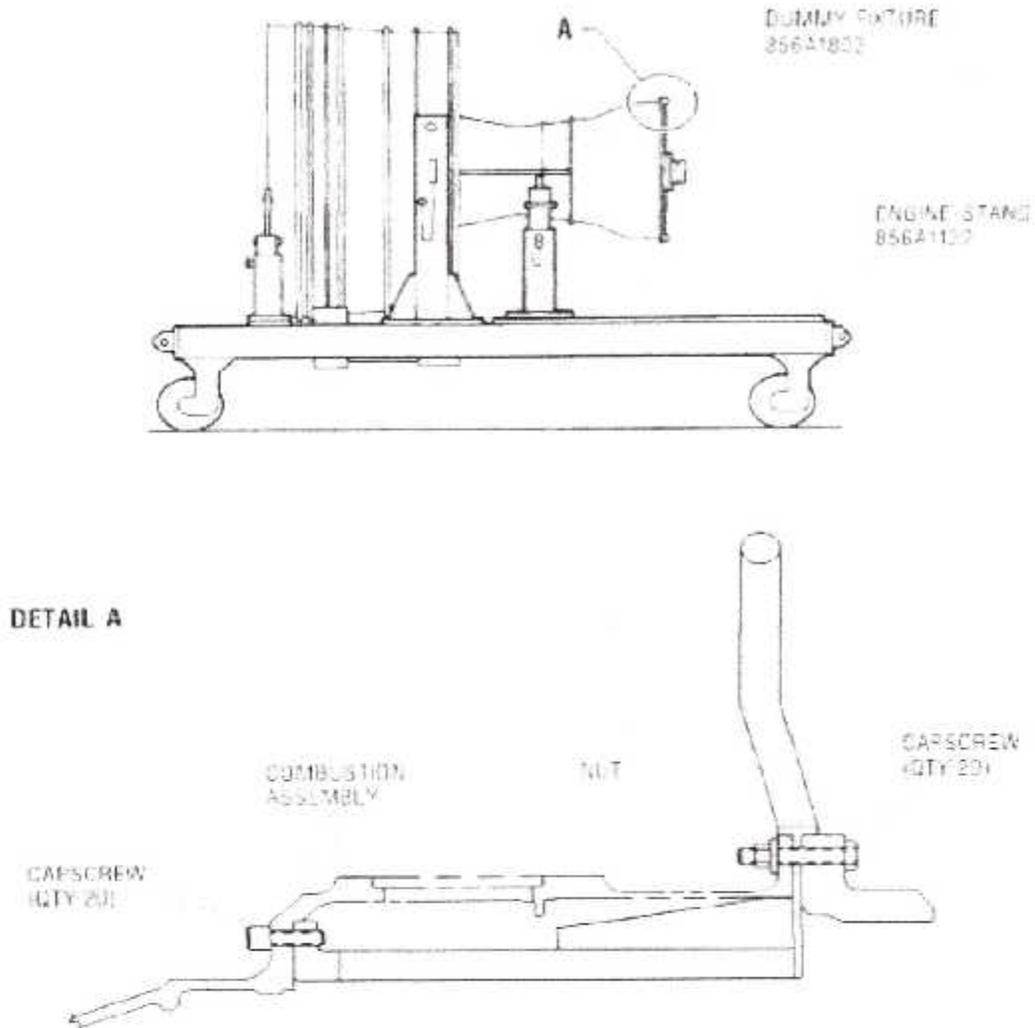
Installation du Dispositif de Protection. Sur le Stator HPT.
